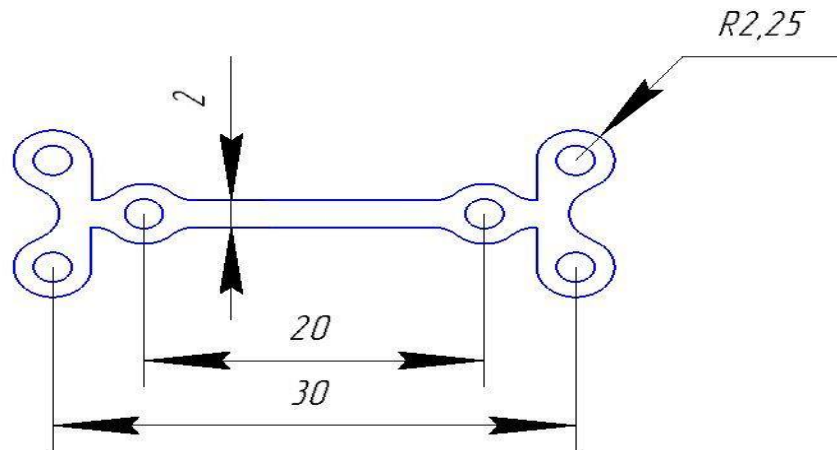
Конструкція пластини у формі кістки типу II з розмірами
